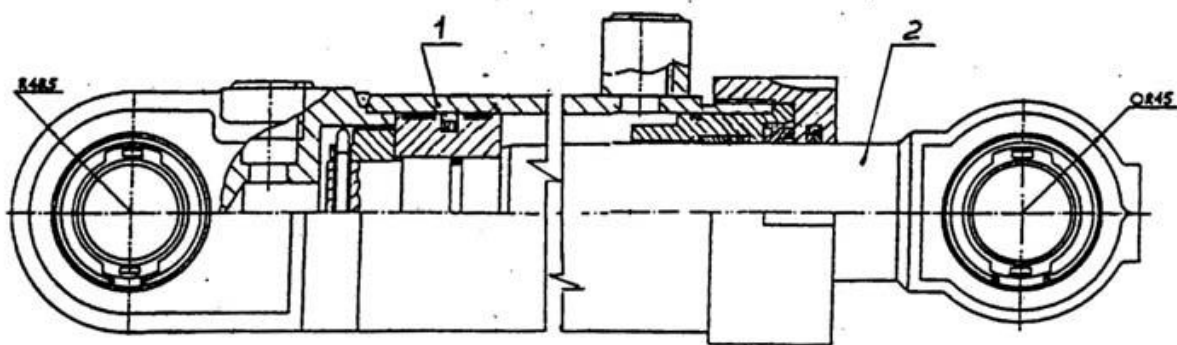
Общий вид: 1 – корпус в сборе; 2 – шток в сборе
